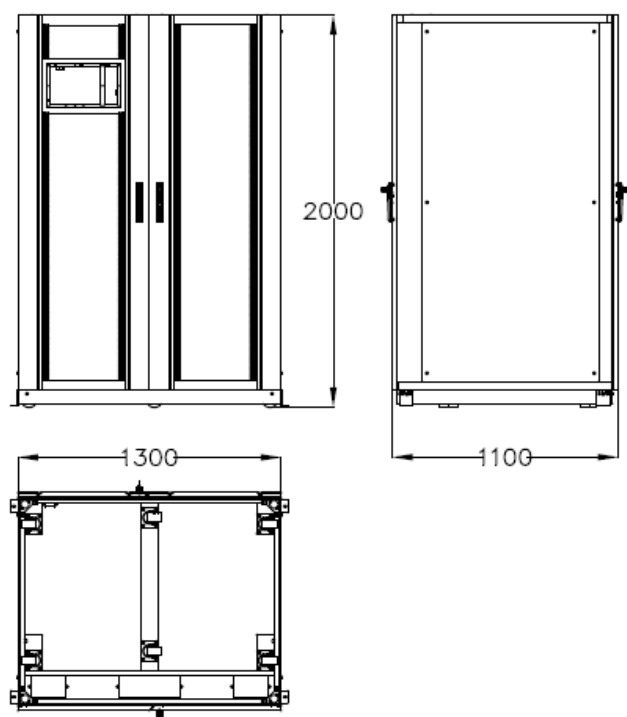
Размер для щитка 400-500КВА (Единицы: мм)
